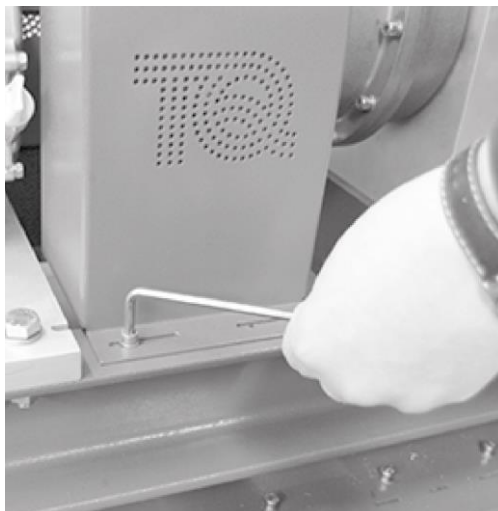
Popraw ułożenie płyty montażowej względem kołków montażowych
